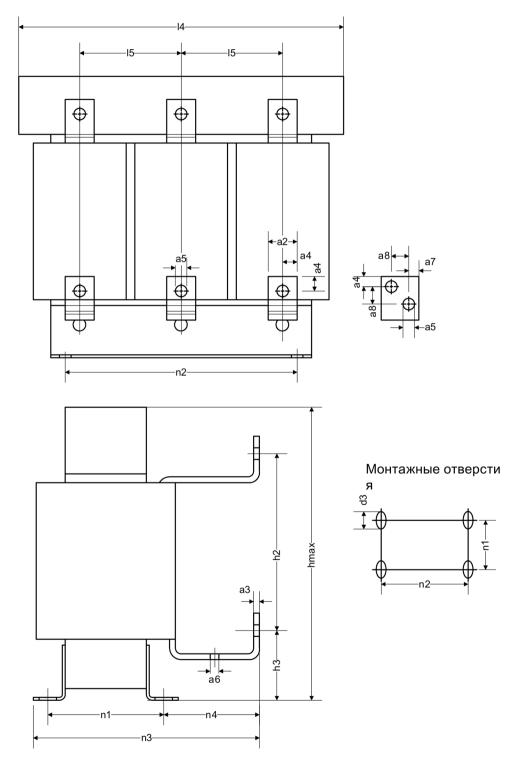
Габаритный чертеж дросселя du/dt
